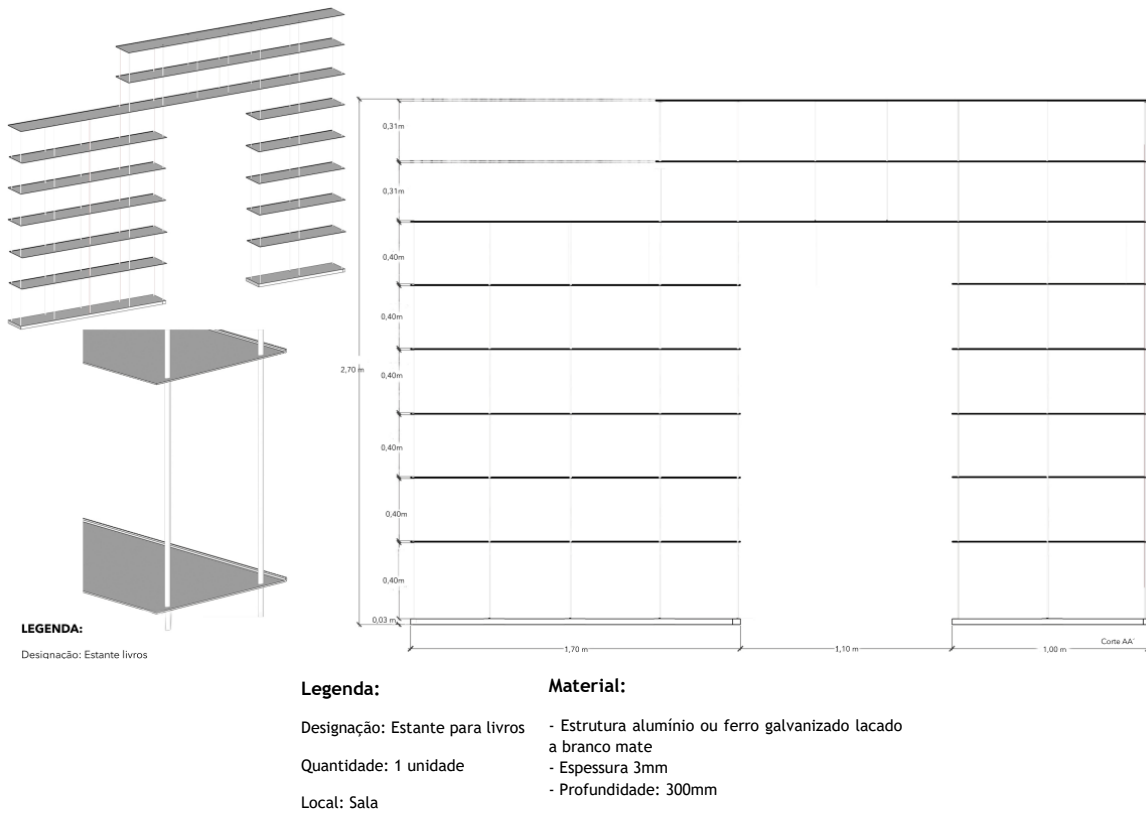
Desenho Técnico Estante Livros. Fonte: Homestories
